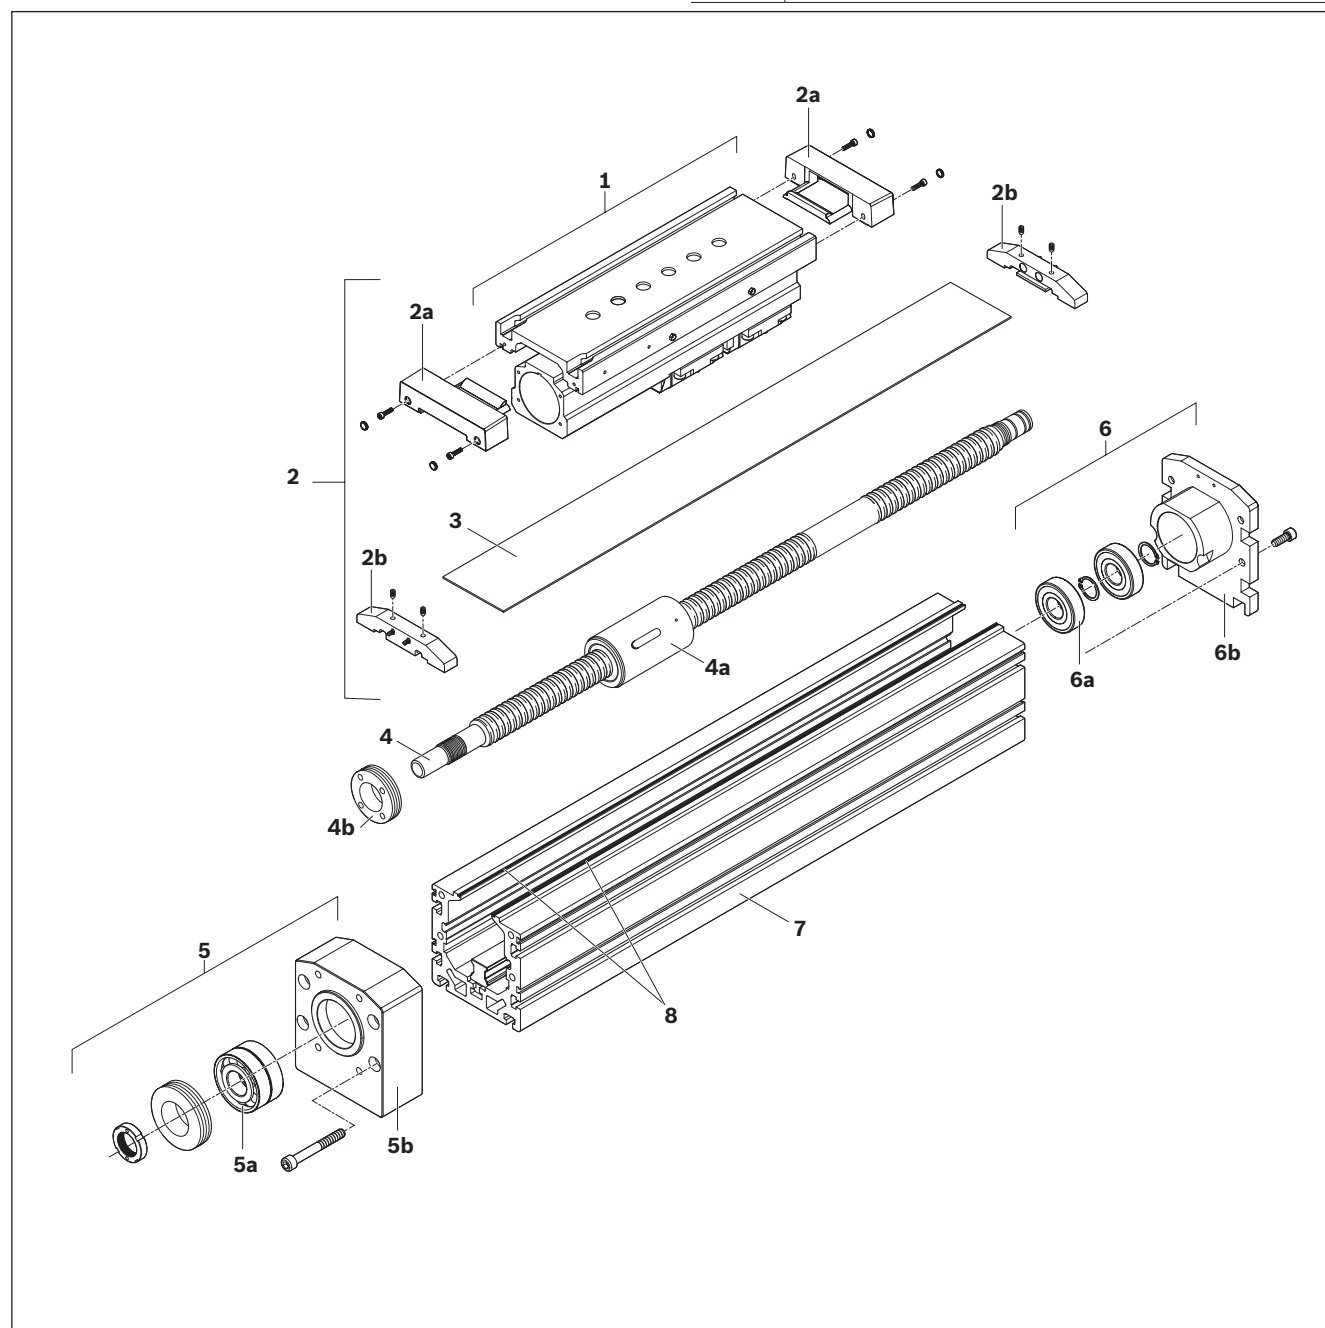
Vue d'ensemble MKK-065/-080/-110-NN-3
